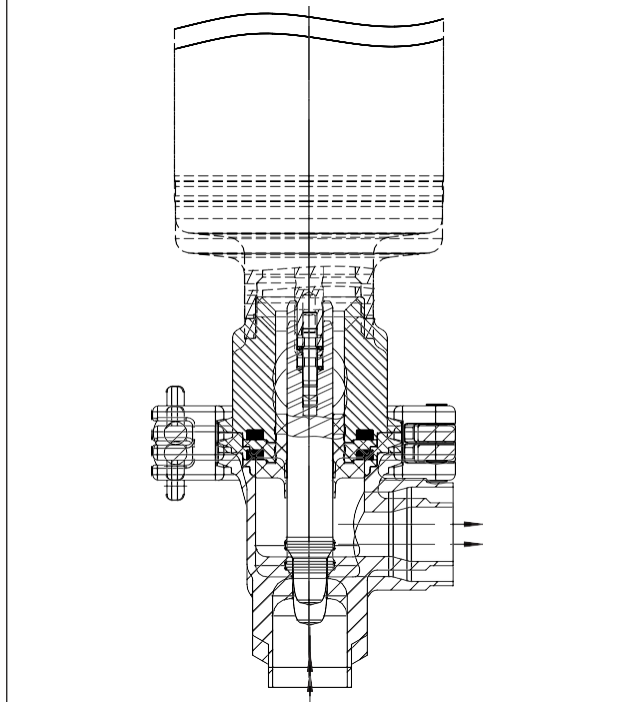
Регулирующий клапан Тип 3347/3379 с концами под приварку. Литое исполнение
